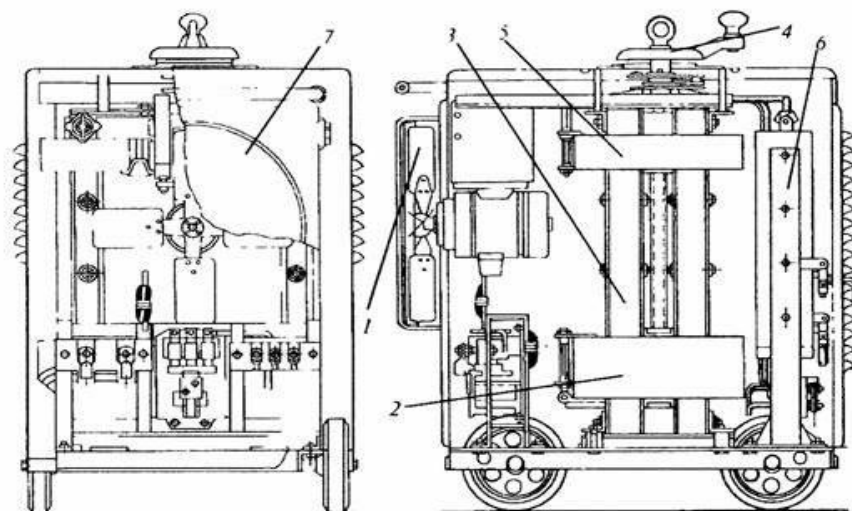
Конструктивная схема сварочного выпрямителя ВСС-300.
